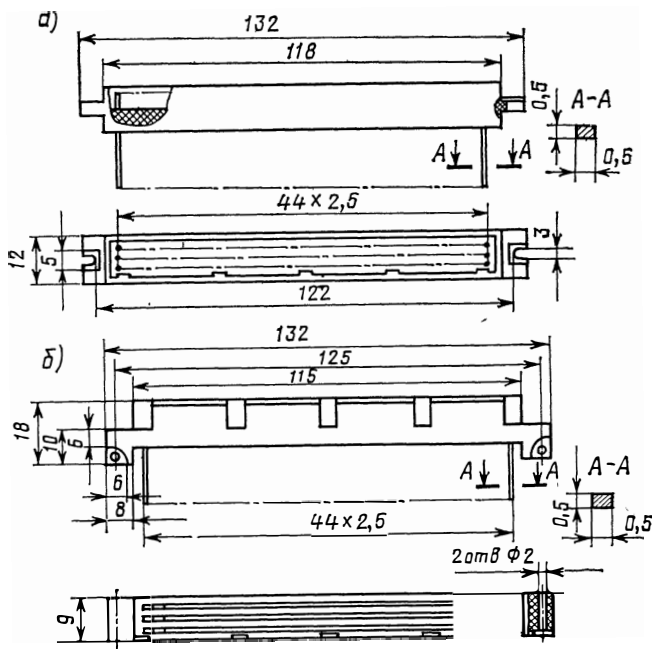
Вилка (а) и розетка (б) соединителя СНП34
